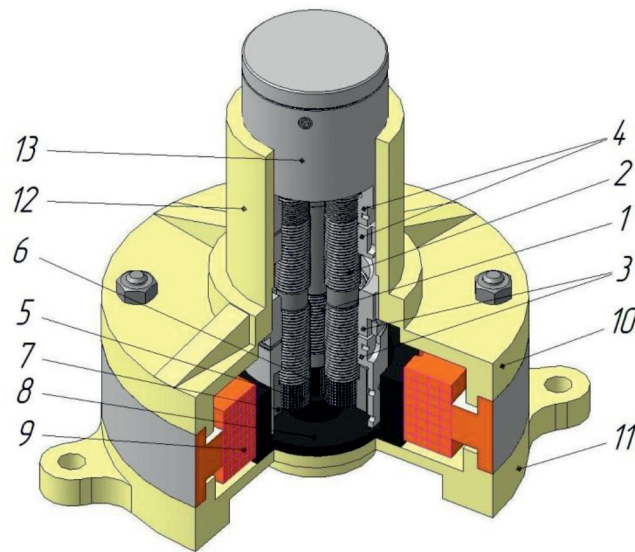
Конструкция актуатора: 1 – винт, 2 – резьбовые ролики-сателлиты, 3 – опорная гайка, 4 – ходовая гайка, 5 – зубчатые венцы роликов, 6 – зубчатые венцы винта, 7 – эпицикл опорной гайки, 8 – ротор шагового двигателя, 9 – статор шагового двигателя, 10 и 11 – крышки корпуса актуатора, 12 – направляющий цилиндр, 13 – шток актуатора
